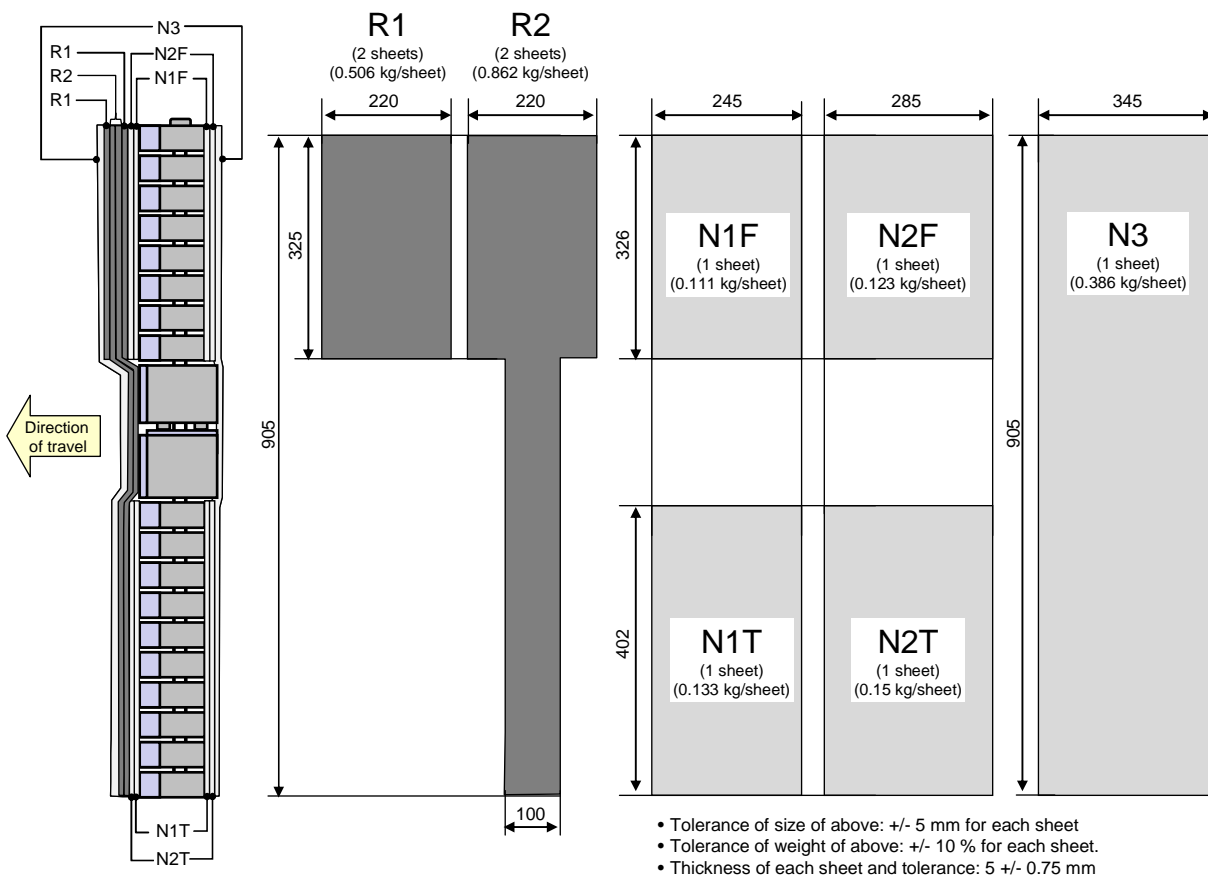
Jambe d'essai FlexPLI: dimensions et masse du garnissage
